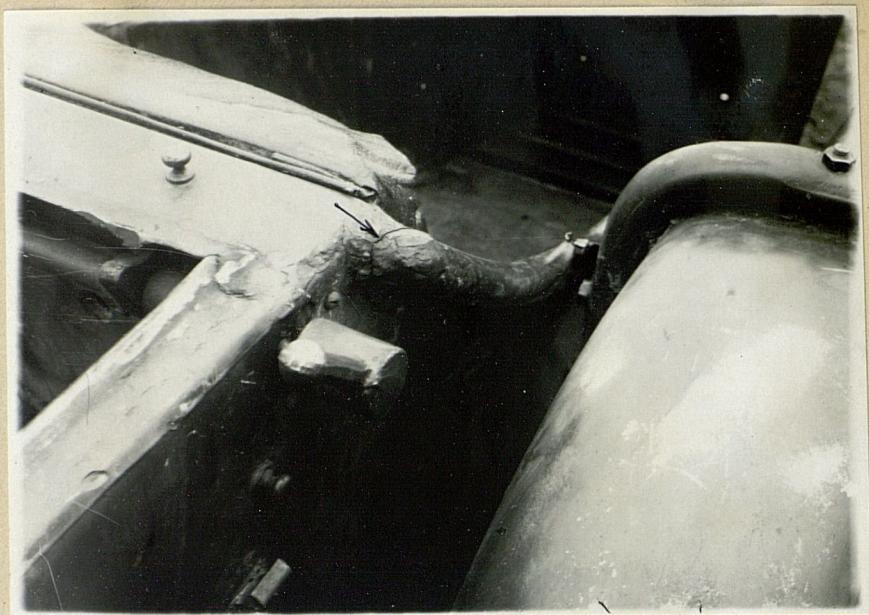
Разрушение сварного шва (указано стрелкой), соединяющего правый стренгер с багажным отделением.
